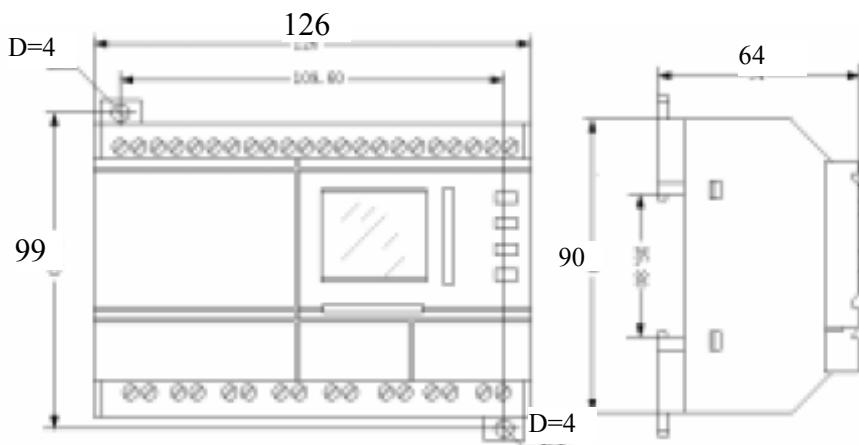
Установочные размеры контроллера SR-22xxxx
